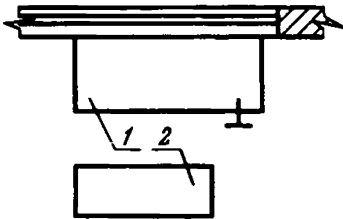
Типовая схема планировки рабочего места разборки карданных валов:
